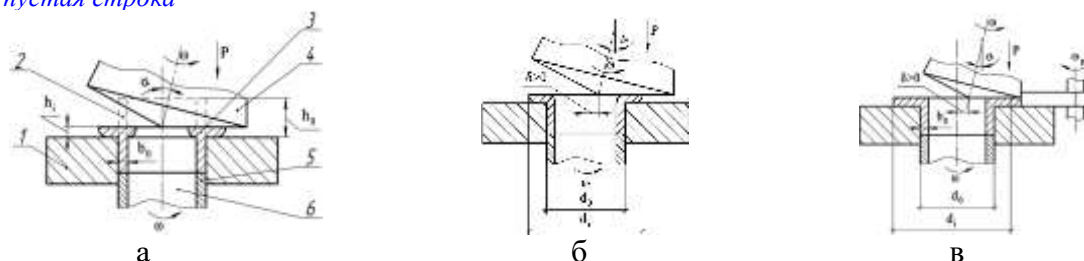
Схемы высадки раскаткой буртов (1 – матрица; 2 – заготовка; 3 – изделие; 4 – валок; 5 – выталкиватель; 6 – оправка):
